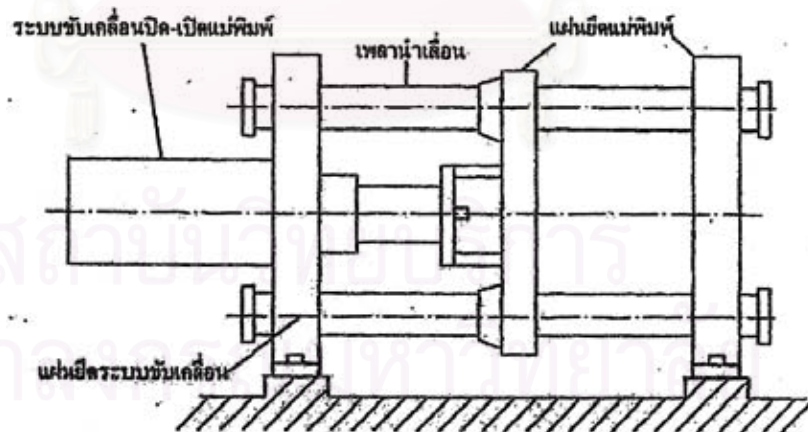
โครงสร้างพื้นฐานของเครื่องฉีดพลาสติก (Injection Molding Machine)
